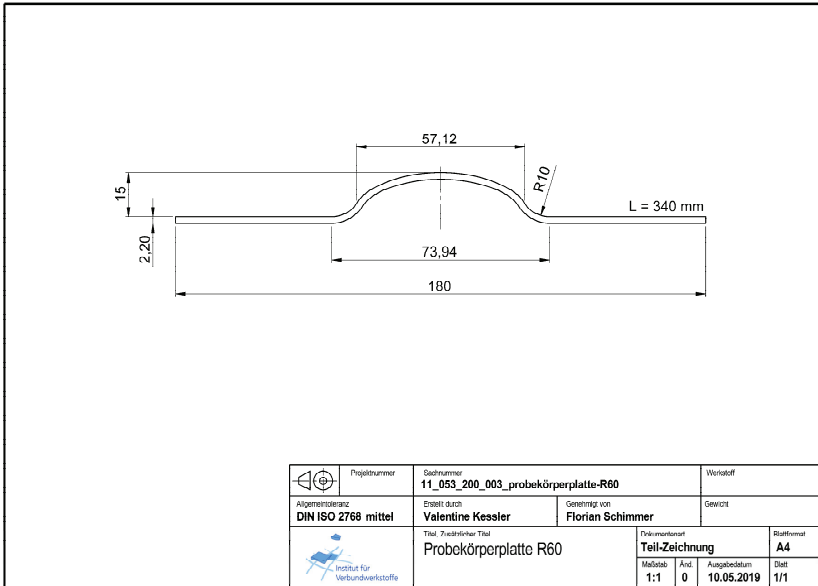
Technische Zeichnung der Ellipse R60 vor PK-Zuschnitt.
